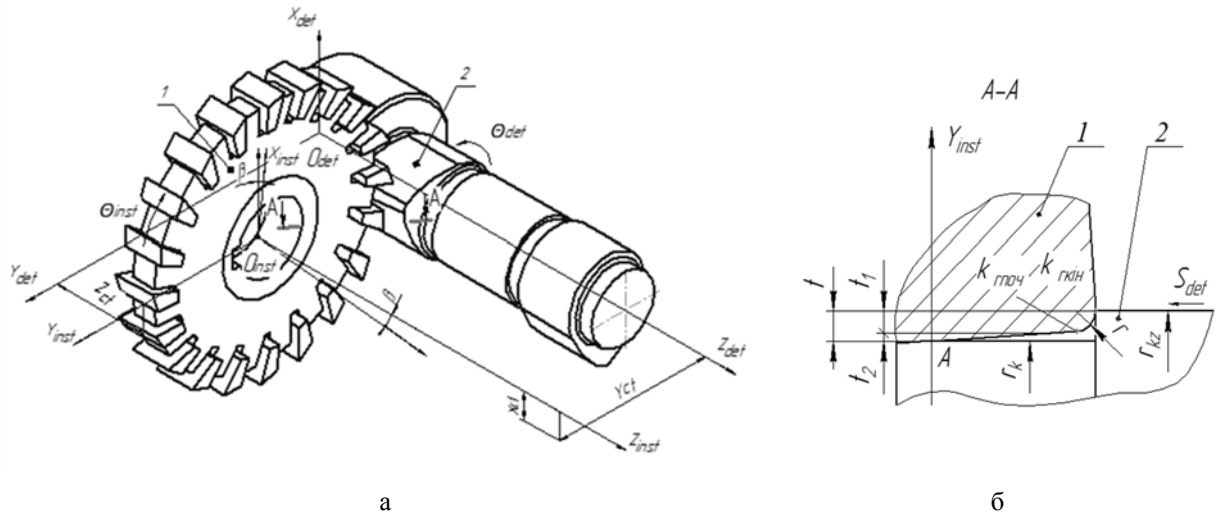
Схема фрезерування кулачка розподільчого вала зі схрещеними осями фрези та деталі
